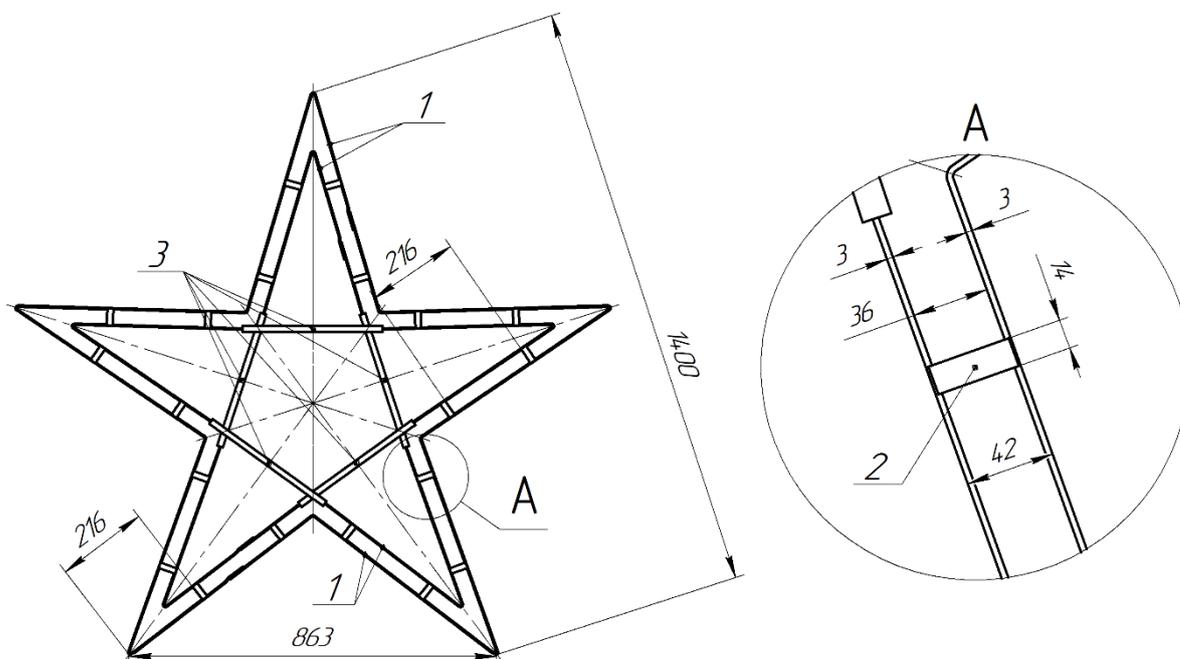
Сварной каркас осветительной конструкции звездообразной формы.
